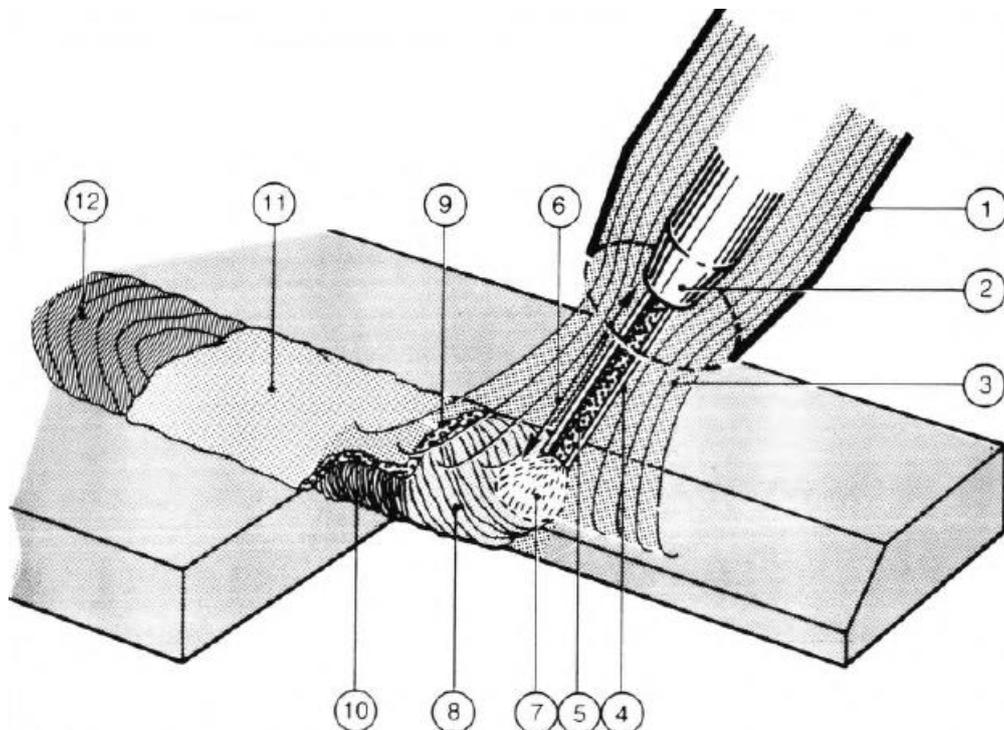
4. Procedimiento de soldadura MIG/MAG. Fuente: [2]
